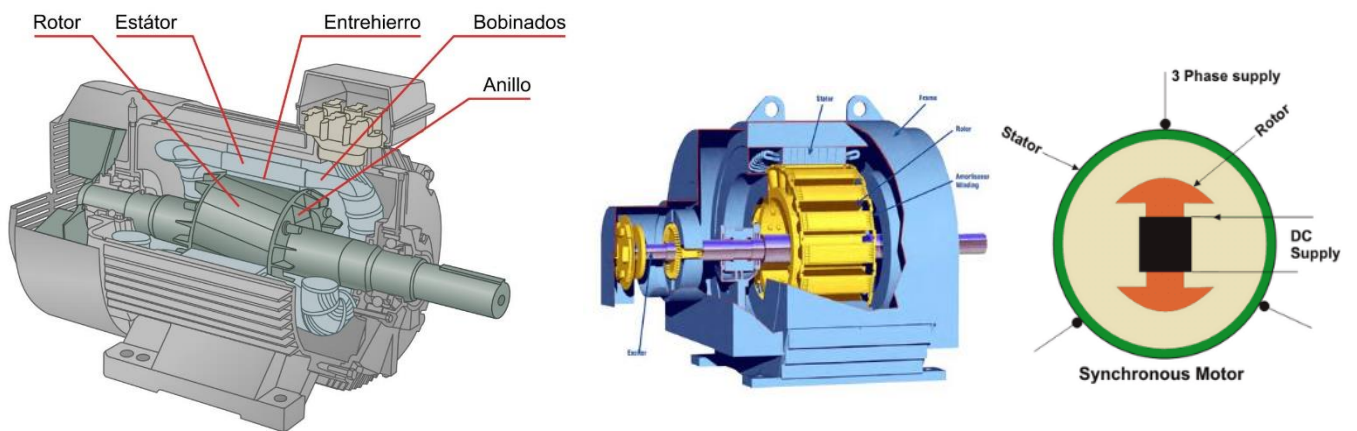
Motor de inducción y sus componentes principales (Izquierda) [38]. Motor síncrono y esquema simplificado (Derecha) [39].
